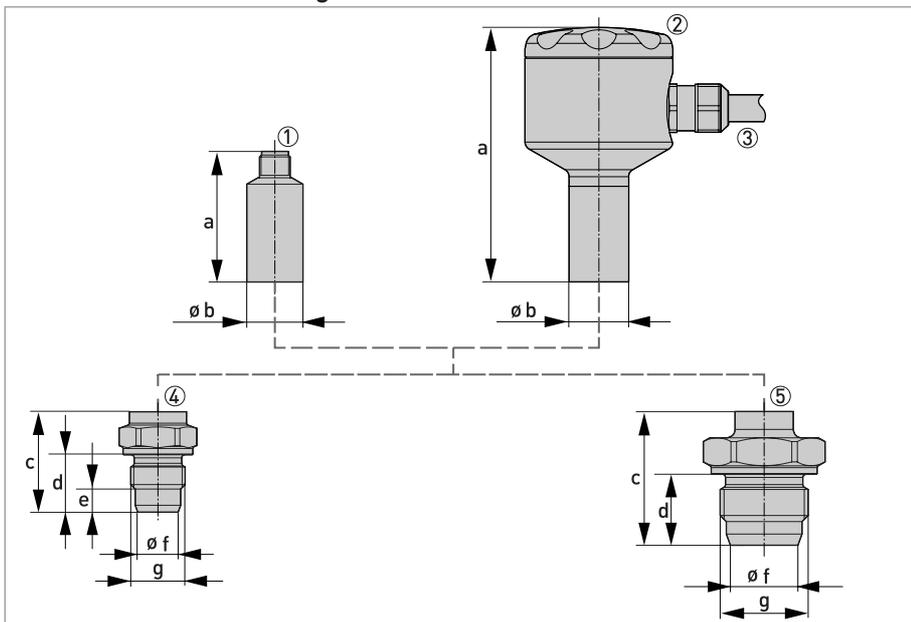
Abmessungen für Drucktransmitter mit Gewinde mit frontbündigem Dichtkonus
